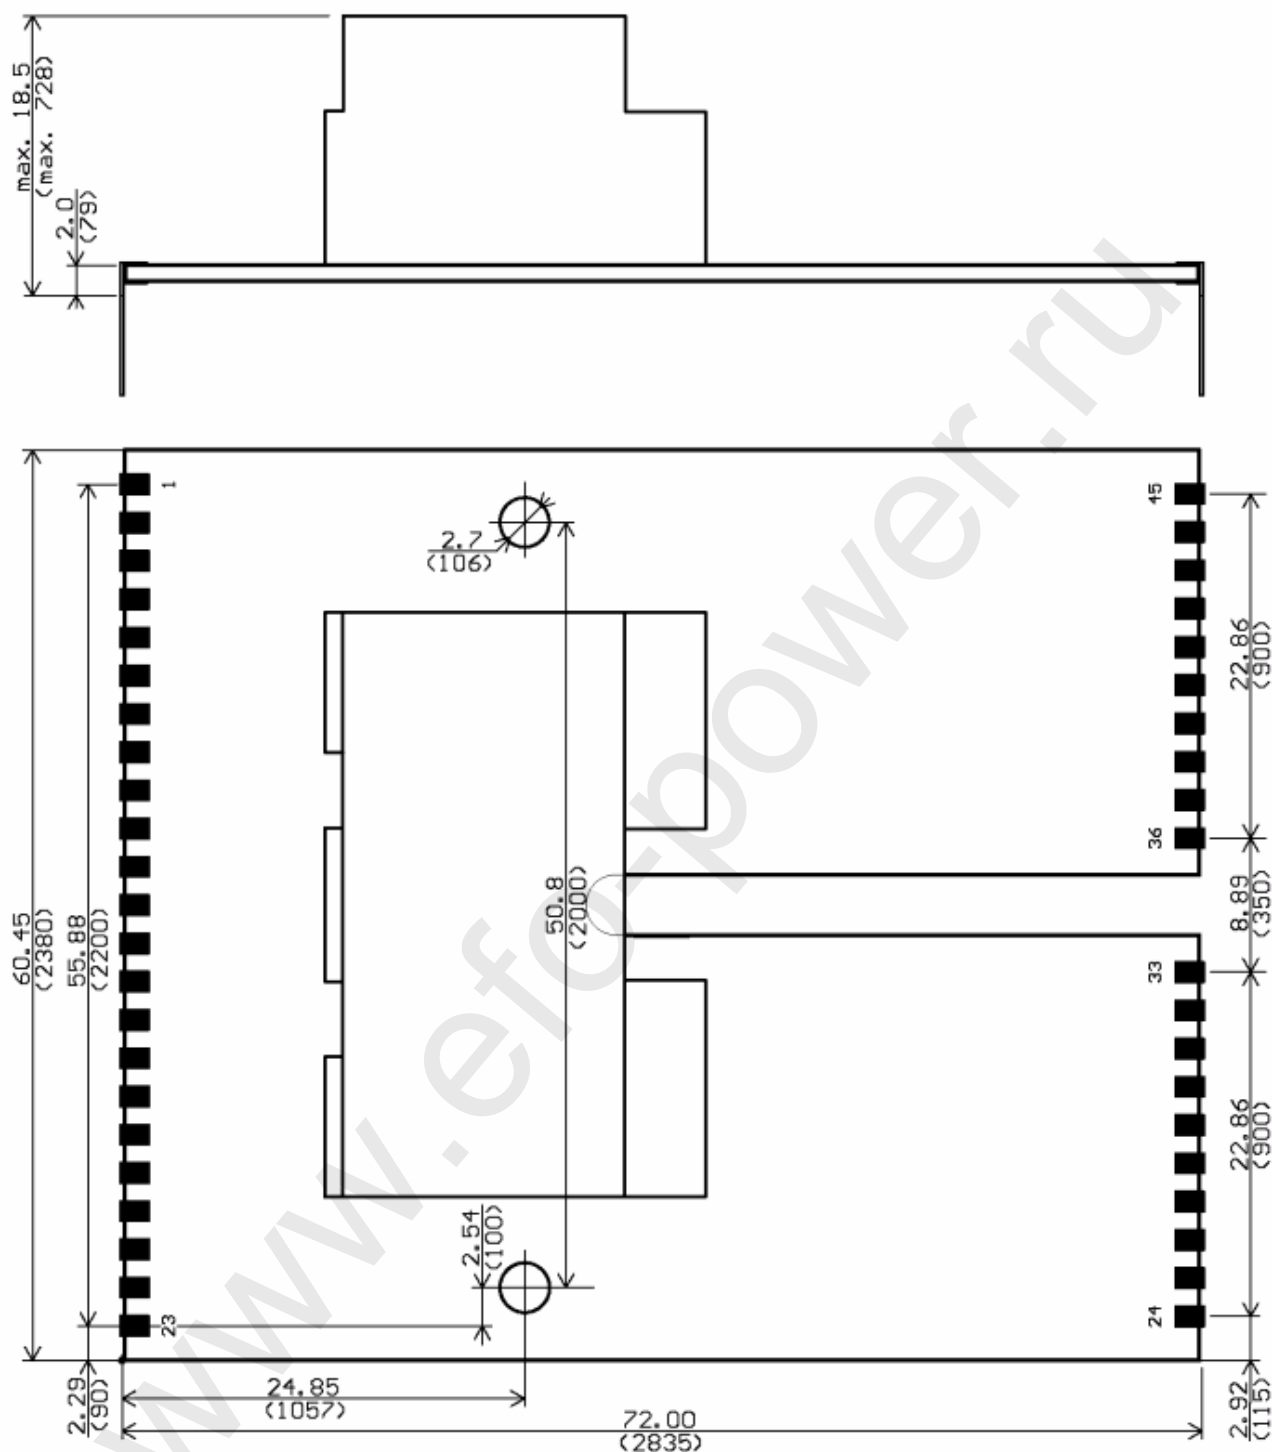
Конструкция драйвера и основные размеры (вид сверху)
